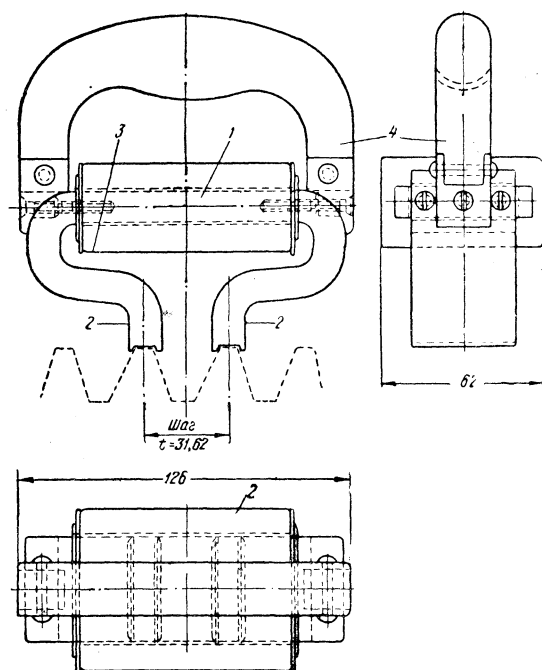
Дефектоскоп для проверки зубчатых колес
